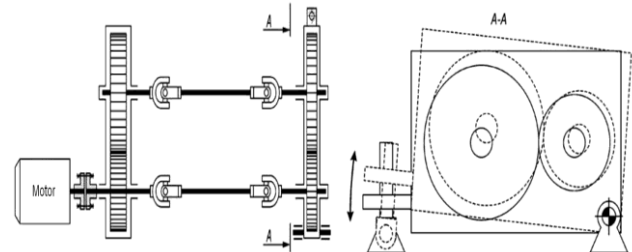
Aplicación del torque mediante rotación de la caja de engranajes completa [40].
